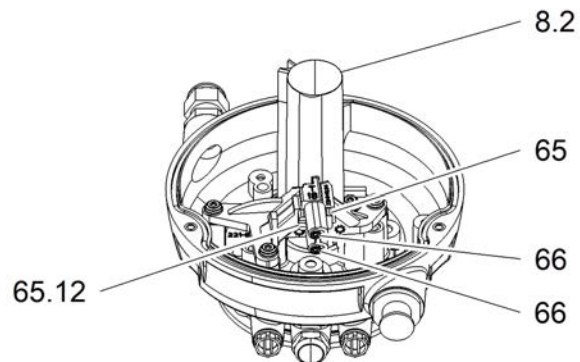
Bloque neumático (8.2) para máx. 1 válvula piloto
